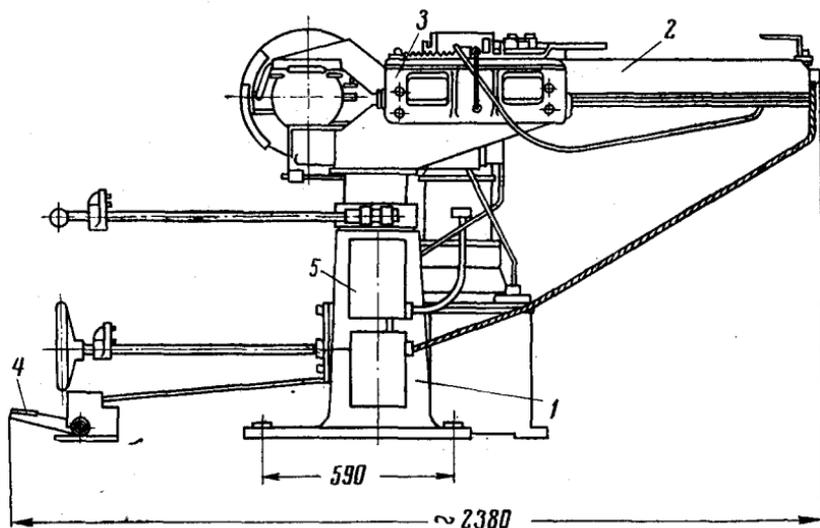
Торцовочный станок с прямолинейным движением суппорта с пилой
